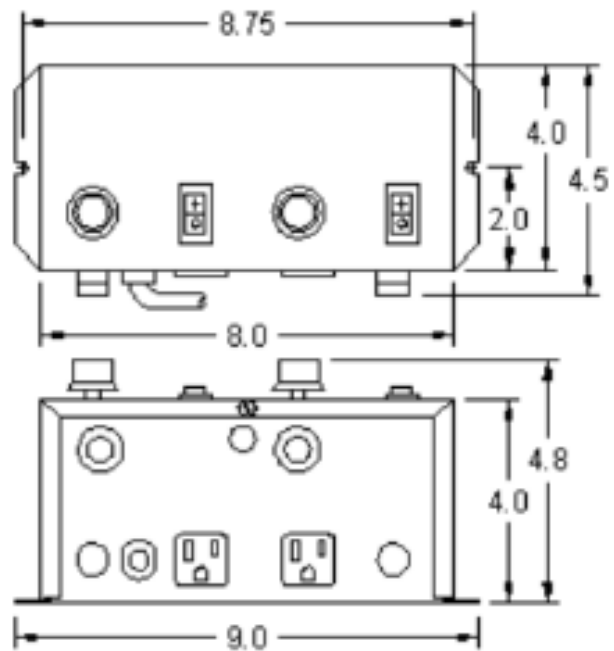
Dimensiones del segundo controlador de vibraciones [30]
